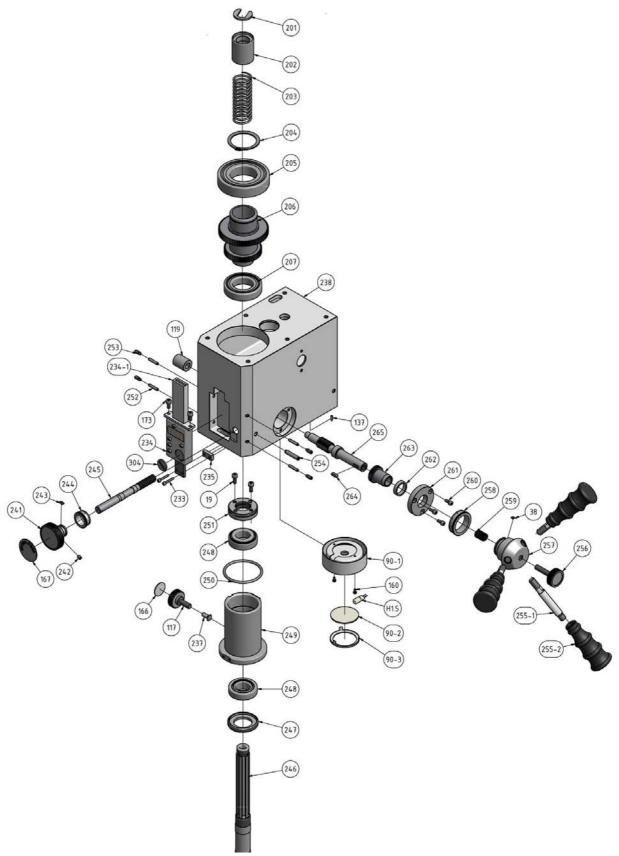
Fräskopf 1 von 2 - Milling head 1 of 2
